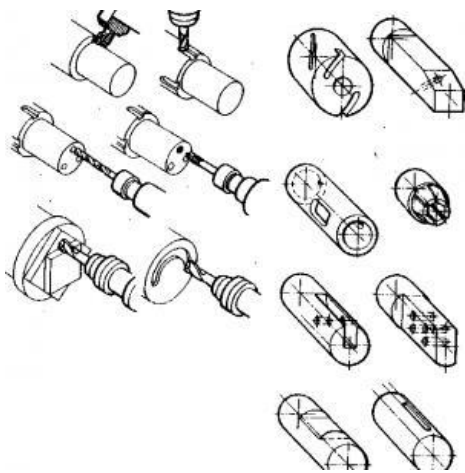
Примеры обработки на станках с револьверной головкой с приводными шпинделями
